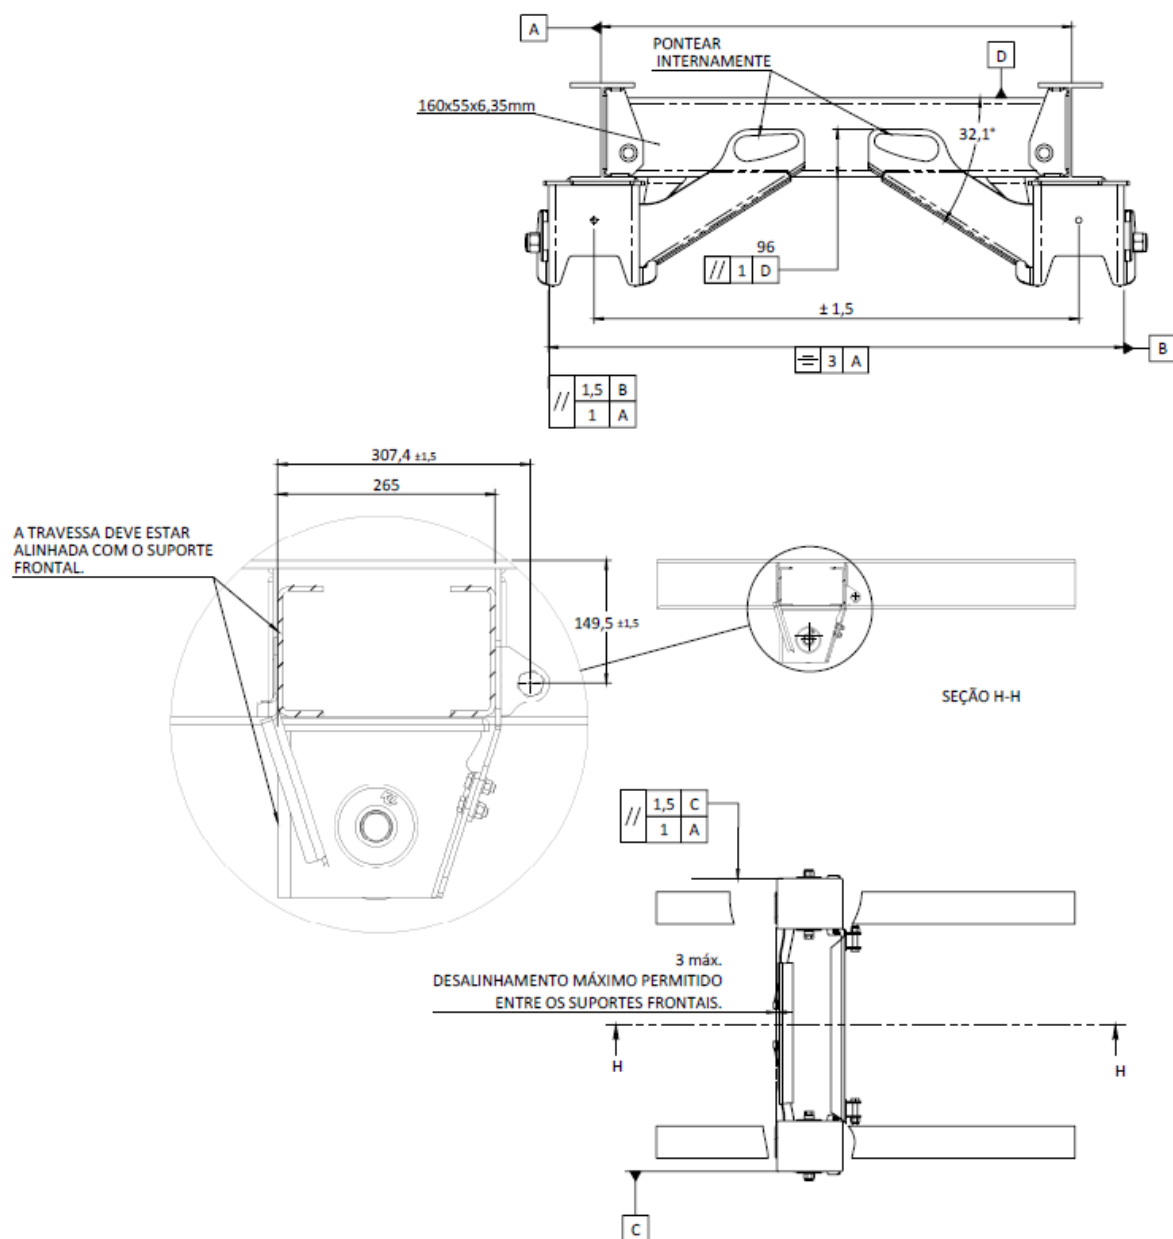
Solda do suporte frontal e reforço de ligação AIRSUPER H210
